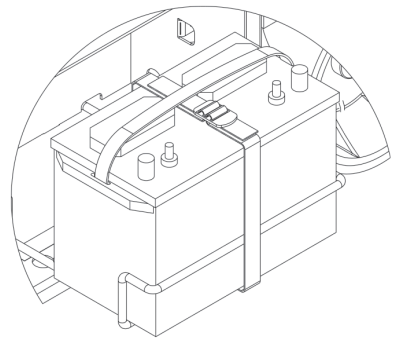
MATENIMIENTO DE LA BATERÍA
